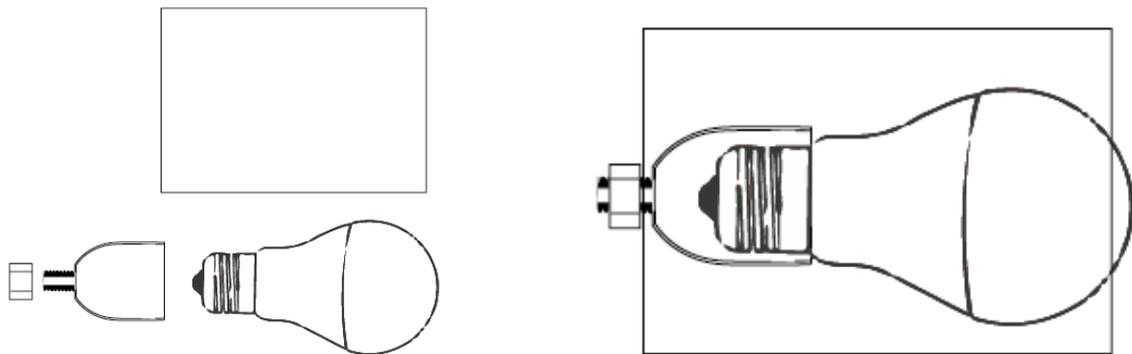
Croquis de unión del casquillo y la bombilla a la pantalla
